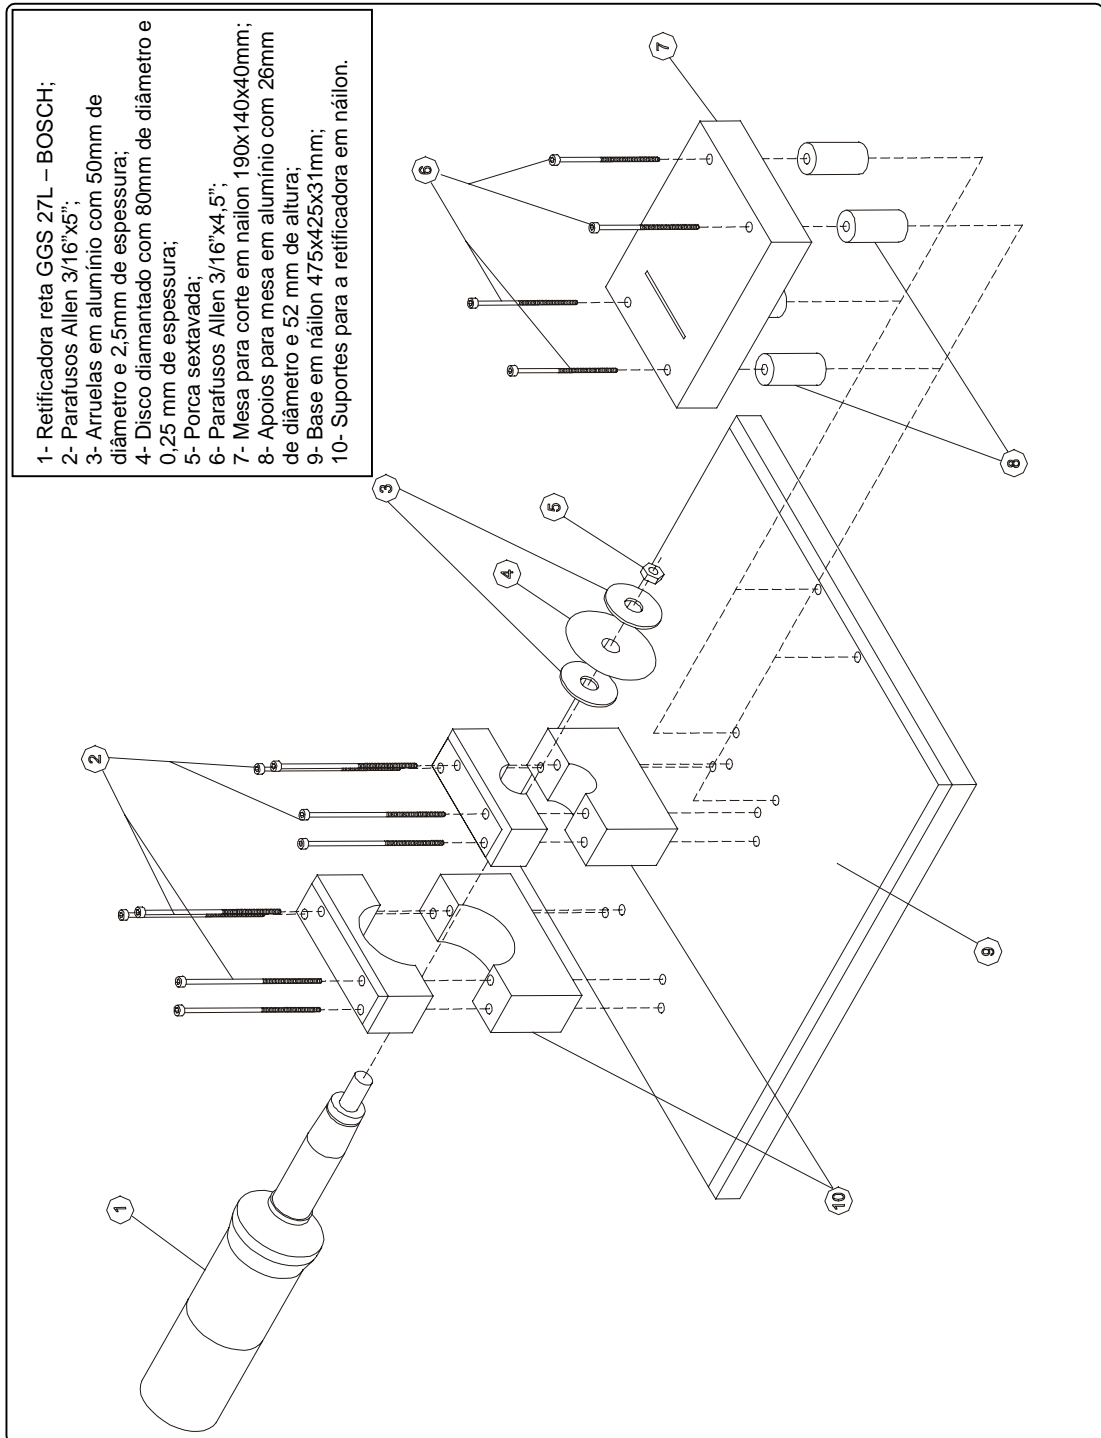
Vista explodida da máquina projetada e construída para serrar material biológico.
